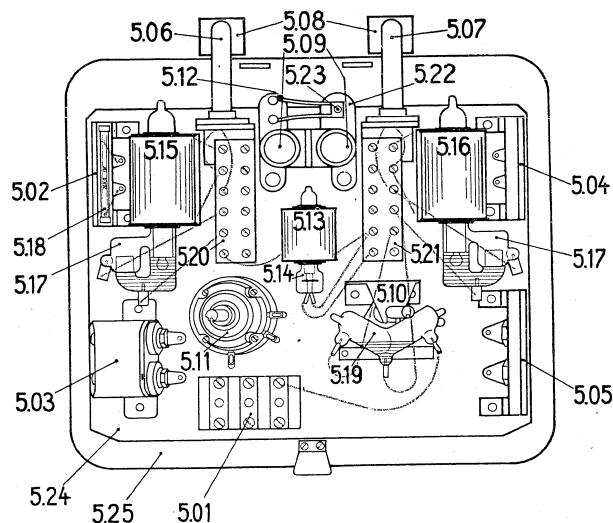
Relais des Universalthermostats in geöffnetem Zustand
